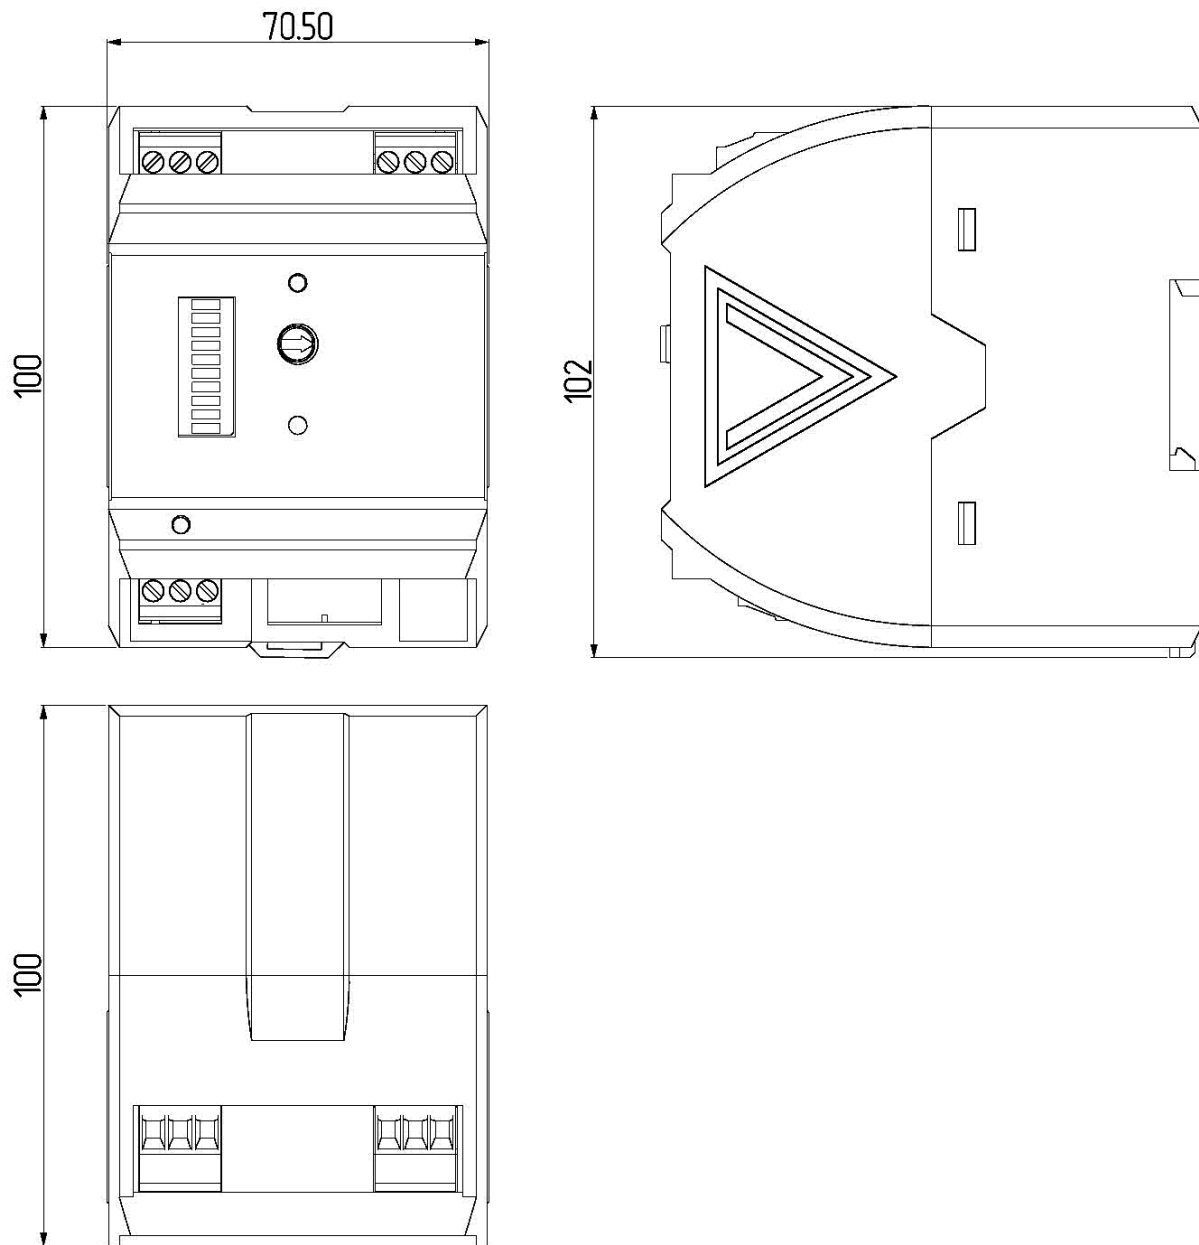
Внешний вид. Габаритный чертёж РКСИ-1002
